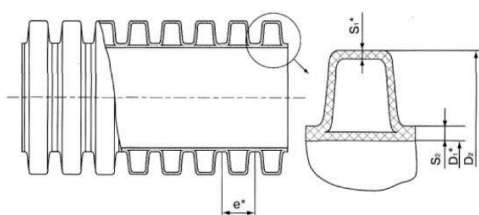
Конструкция и основные размеры гофрированной двухслойной трубы из полиэтилена
